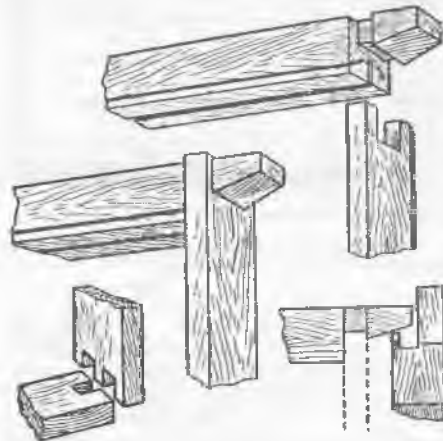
Детальное изображение угла рамки и верхнего угла корпуса улья с металлической опорой для рамки.
